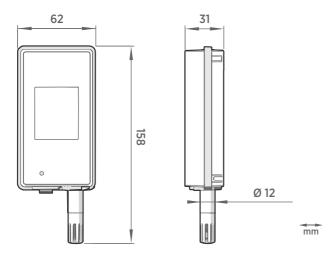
Dimensiones del RFL100 sin el soporte de montaje
